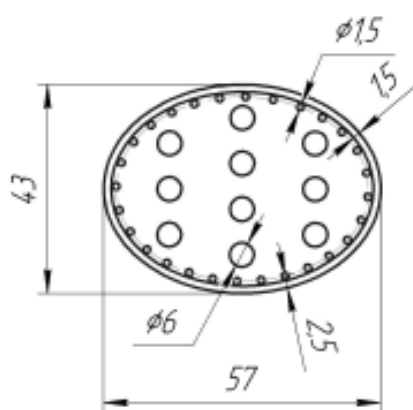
Чертёж основы нашивки для печати на 3D-принтере
